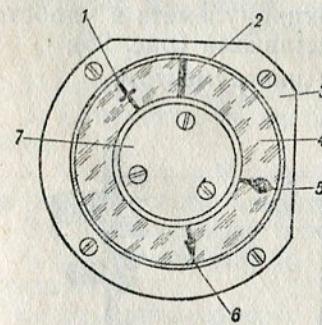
Передняя стенка корпуса кинопулемета (вид спереди на часы-секундомер)
